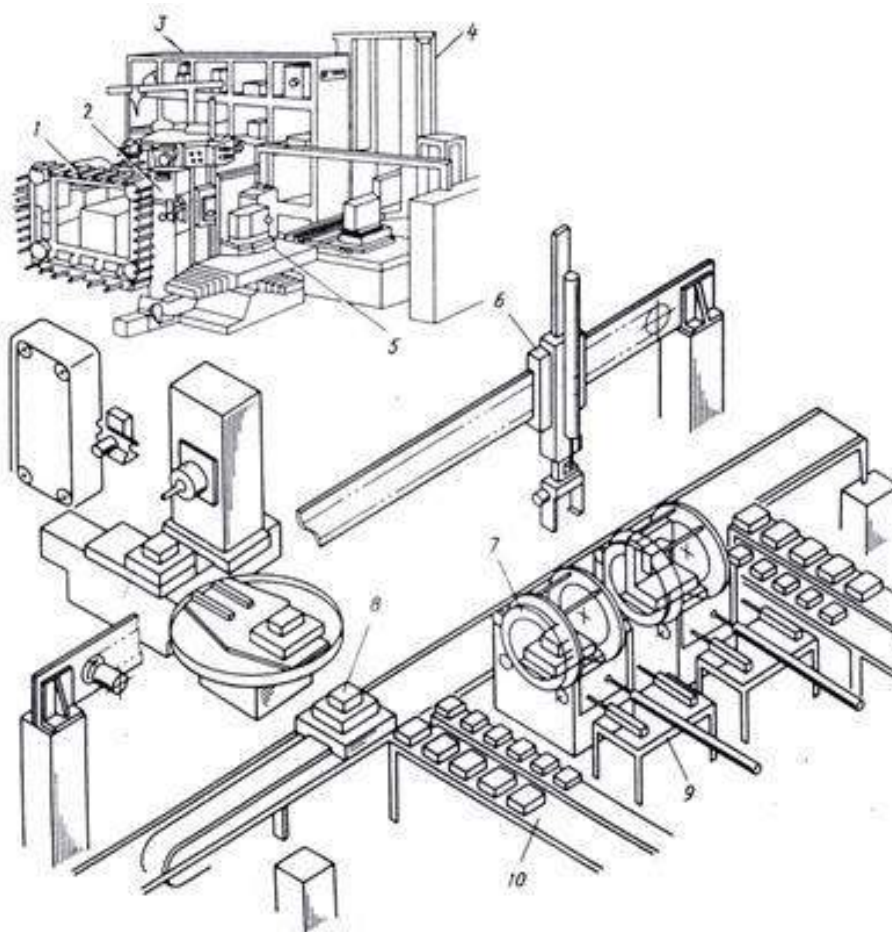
Транспортирование и подача заготовок к станку: 1 — цепной инструментальный магазин; 2 — горизонтальный многоцелевой станок; 3 — склад-накопитель; 4 кран-штабелер; 5 — стол с управлением по восьми координатам; 6 — манипулятор; 7 — реверсивное устройство; 8 — платформа для перемещения спутников; 9 — толкатель; 10 — транспортер
